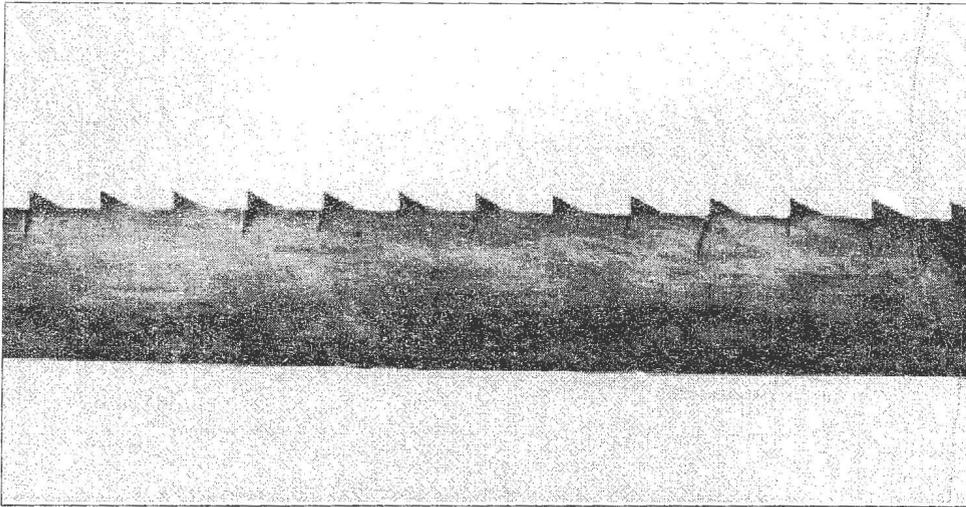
Hoja de sierra sinfín, con grietas en el borde dentado.
